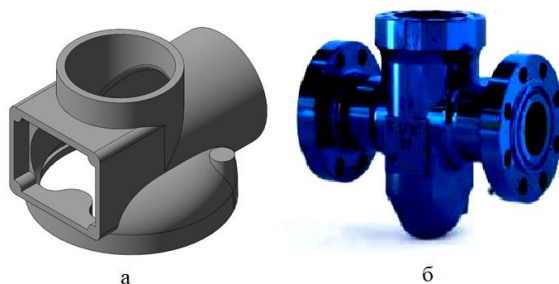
3D-изображение отливок: а – «Переходник»; б – «Корпус»
